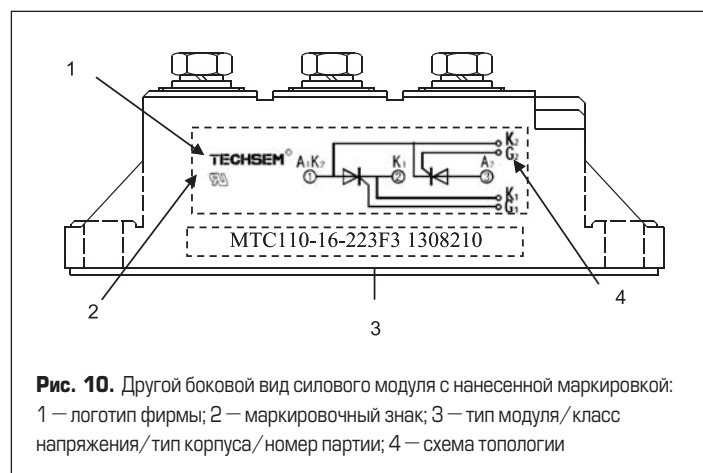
Другой боковой вид силового модуля с нанесенной маркировкой: 1 — логотип фирмы; 2 — маркировочный знак; 3 — тип модуля/класс напряжения/тип корпуса/номер партии; 4 — схема топологии
